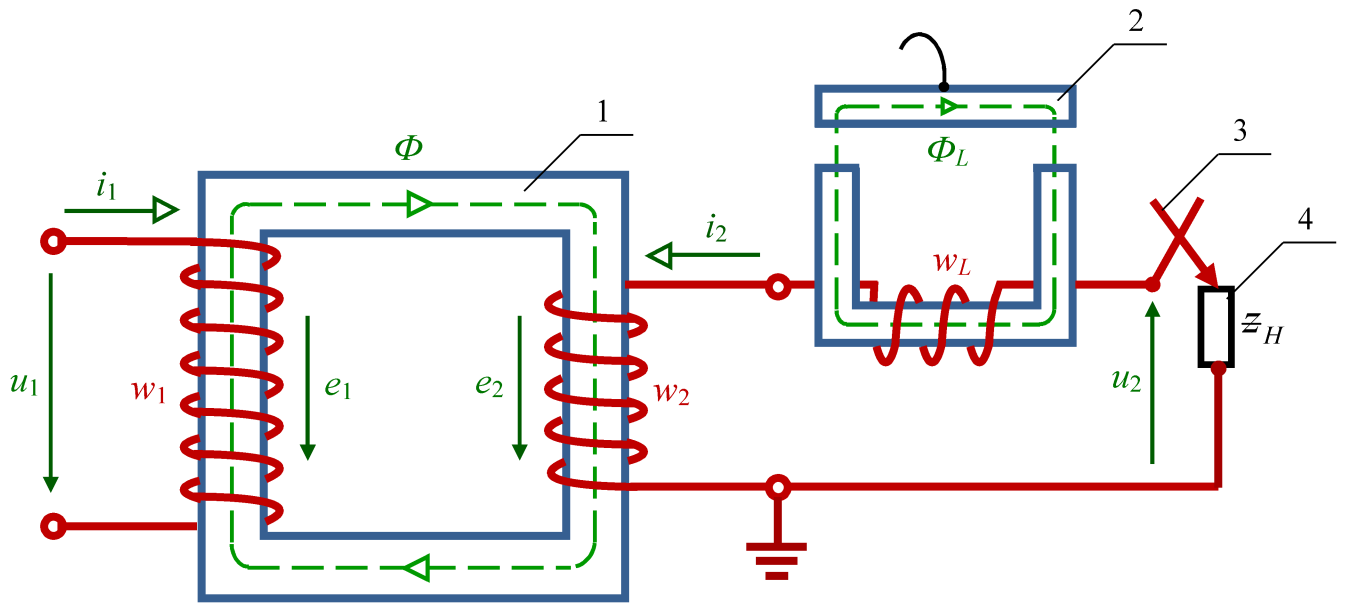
Конструктивна схема однофазного зварювального трансформатора
